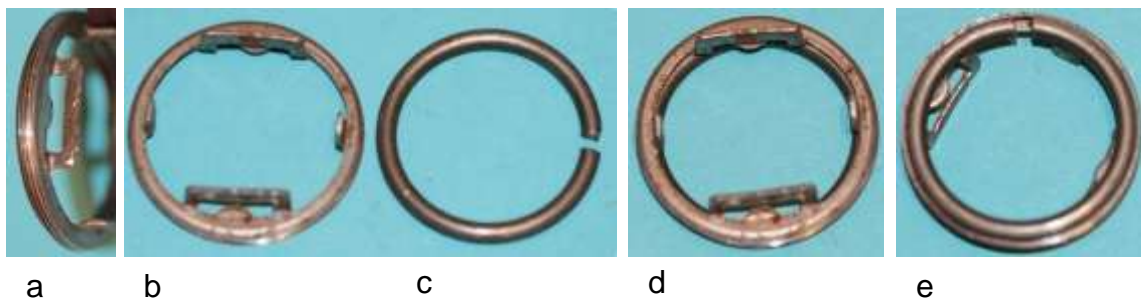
Gewindering: a) und b) Außenseite mit Gewinde und Klemmtasche,
